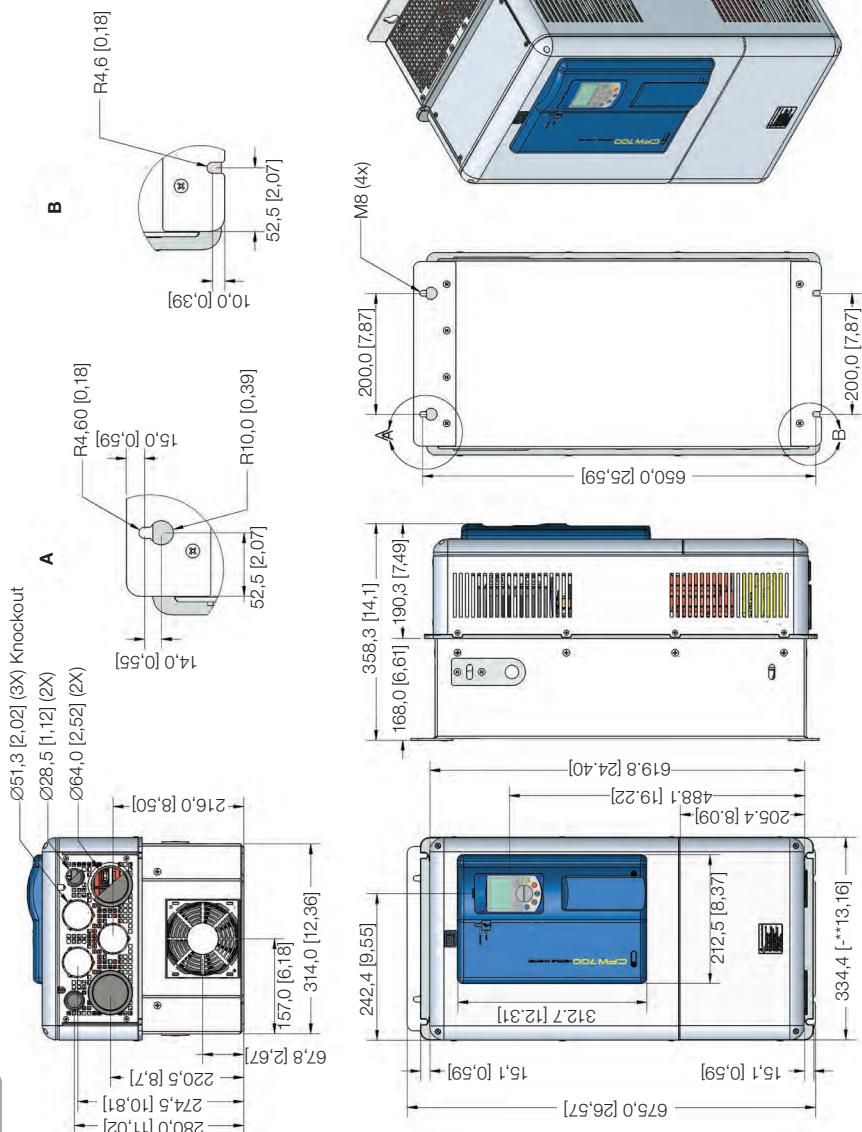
Umrichterbaugröße in mm [in] - gehäuse E
